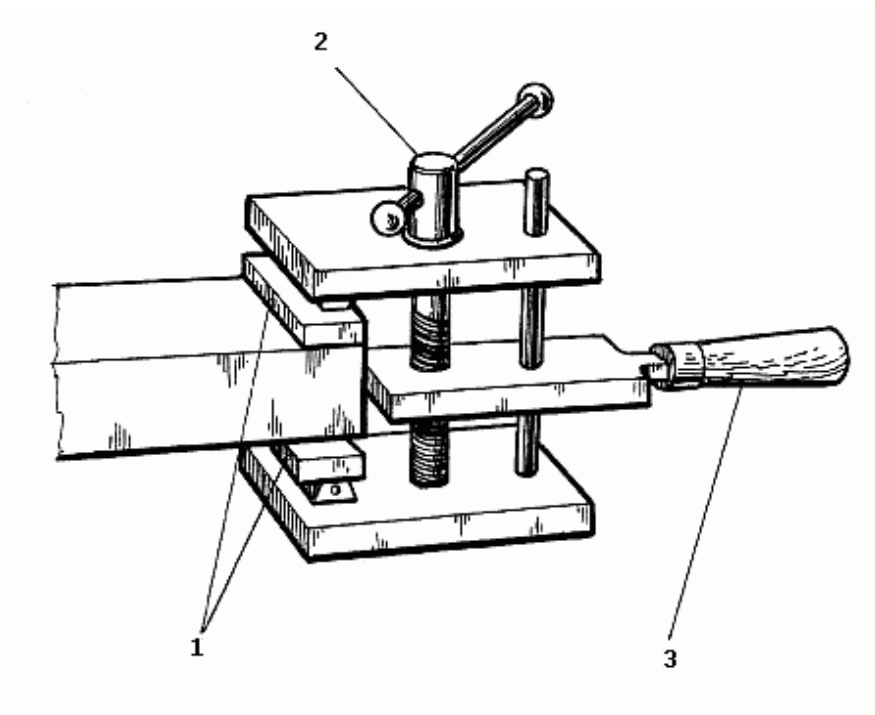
Тисочки-струбцины: 1 – губки; 2 – винт с рукояткой; 3 – ручка
